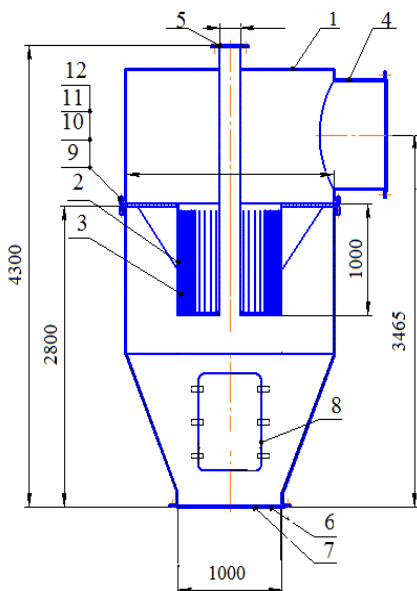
Установка для сушіння післяспиртової барди: 1 – сушильна камера; 2 – уловлювач продукту; 3 – отвори; 4 – вихідний патрубок; 5 – вхідний патрубок; 6 – газорозподільна решітка; 7 – вхід теплоносія; 8 – люк; 9 – болти; 10 – гайки; 11 – шайба; 12 – прокладка
